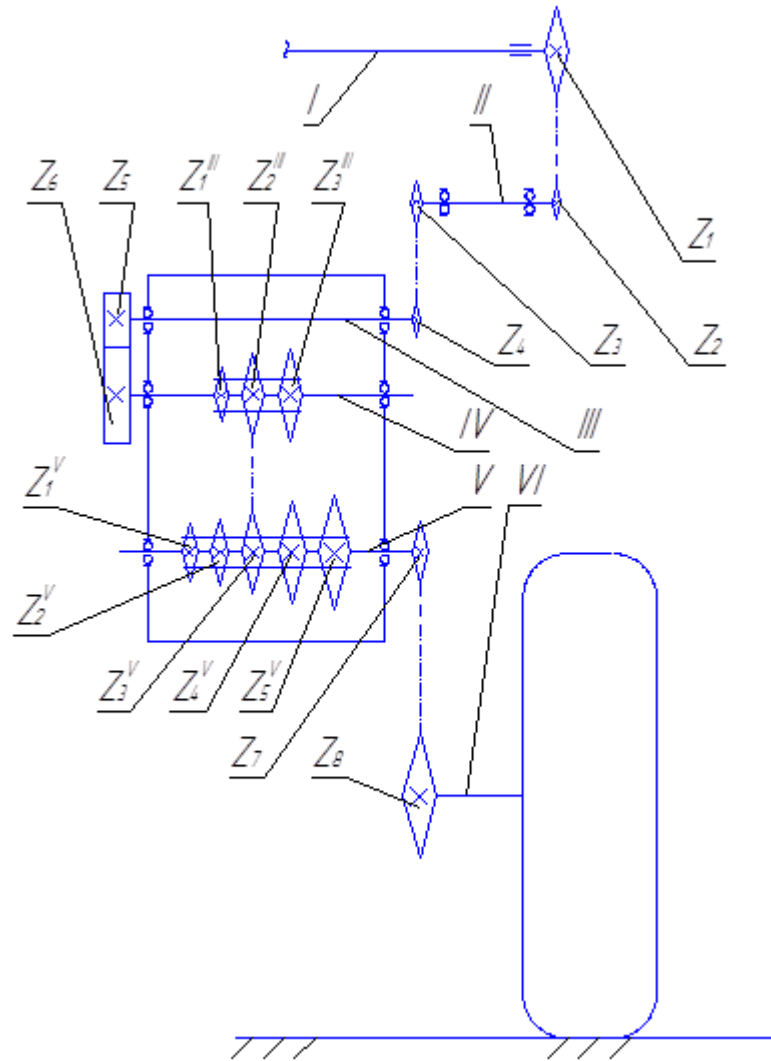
Схема приводу висіваючих апаратів: *I* – вал висіваючих апаратів; *II* – проміжний вал; *III* – вихідний вал касети; *IV* – вихідний вал коробки зміни передач; *V* – вхідний вал коробки зміни передач; *VI* – вал опорно-приводного колеса.
